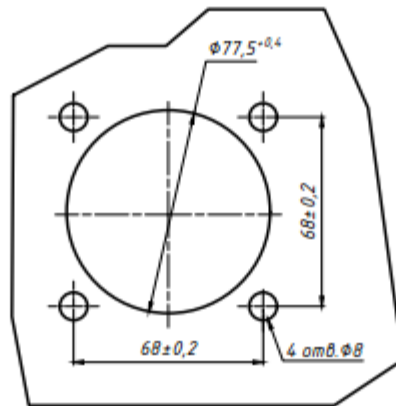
Габаритный чертеж приборов М1420, М1420.1
